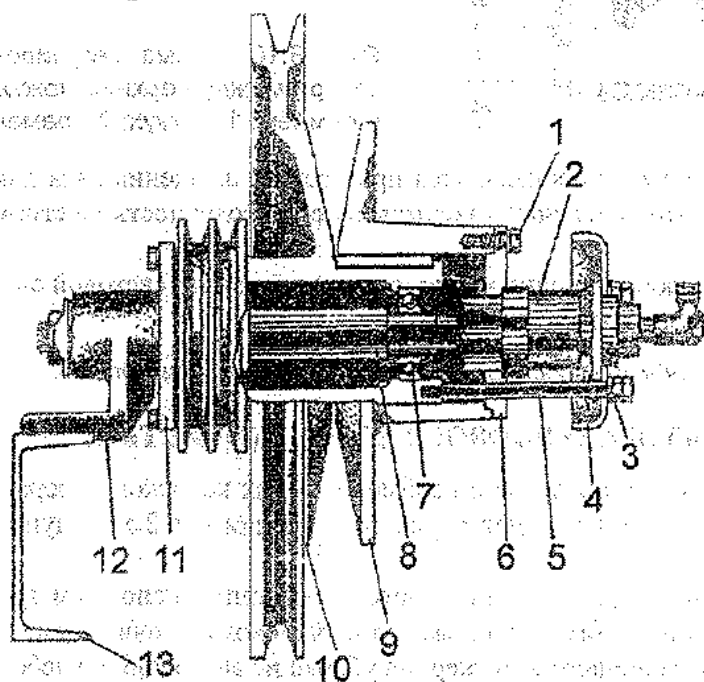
Контрпривод вентилятора: 1 - регулировочный винт; 2 - гидроцилиндр; 3 - регулировочная шайба; 4 - тарелка опорная; 5 - палец; 6 - фланец; 7 - подшипник 180206; 8 - вал контрпривода; 9 - диск подвижный; 10 - диск неподвижный; 11 - крышка подшипника; 12 - кронштейн; 13 - швеллер рамы молотилки
